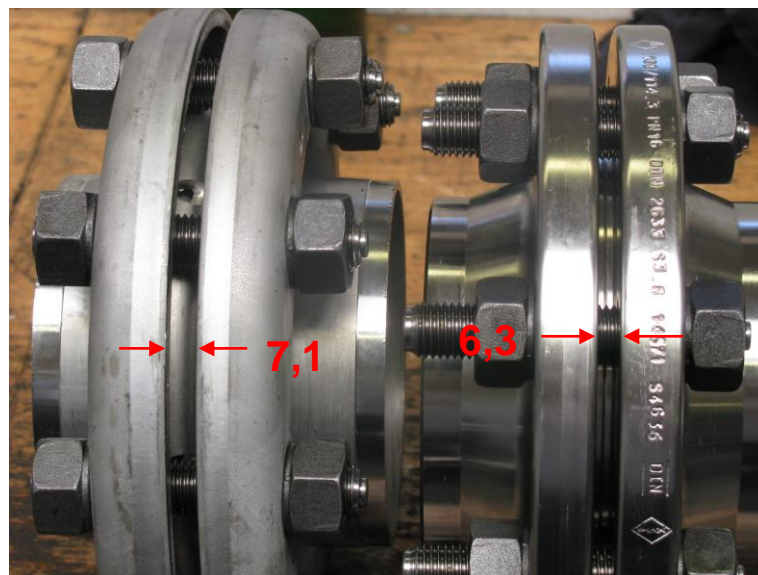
Flanschverbindungen nach Aufbringung der Schraubenkräfte mit 180 Nm
